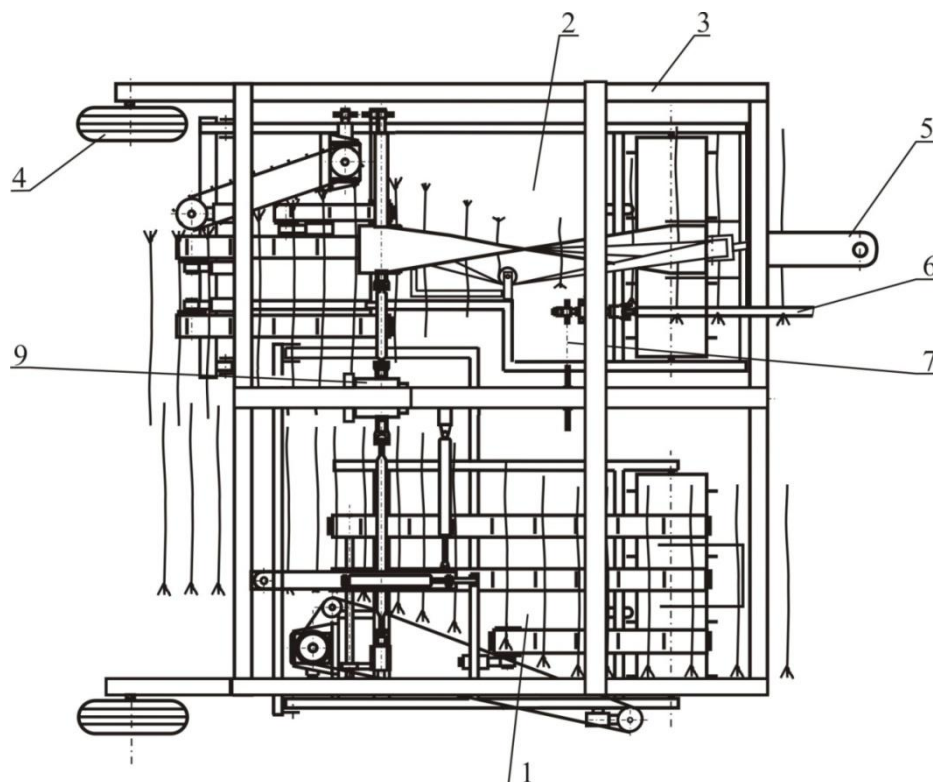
Схема сдваивателя лент тресты, вид сверху
